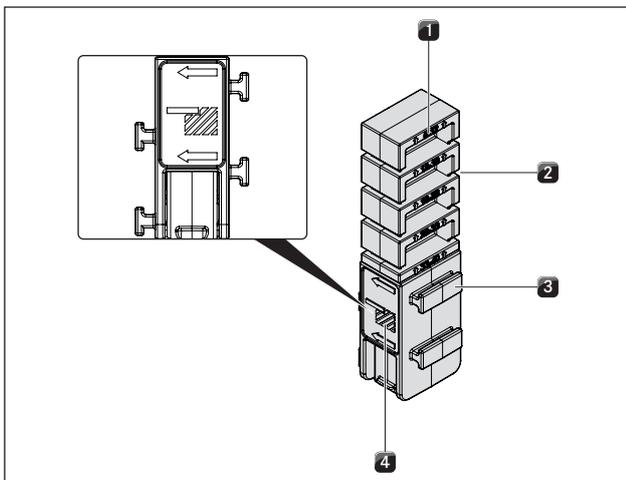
Borna de montaje lado derecho (montaje enrasado)
